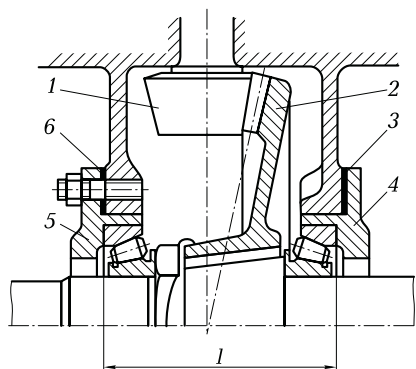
Схема одновременного регулирования зацепления конических зубчатых колес и зазора в роликовых радиально-упорных подшипниках:
